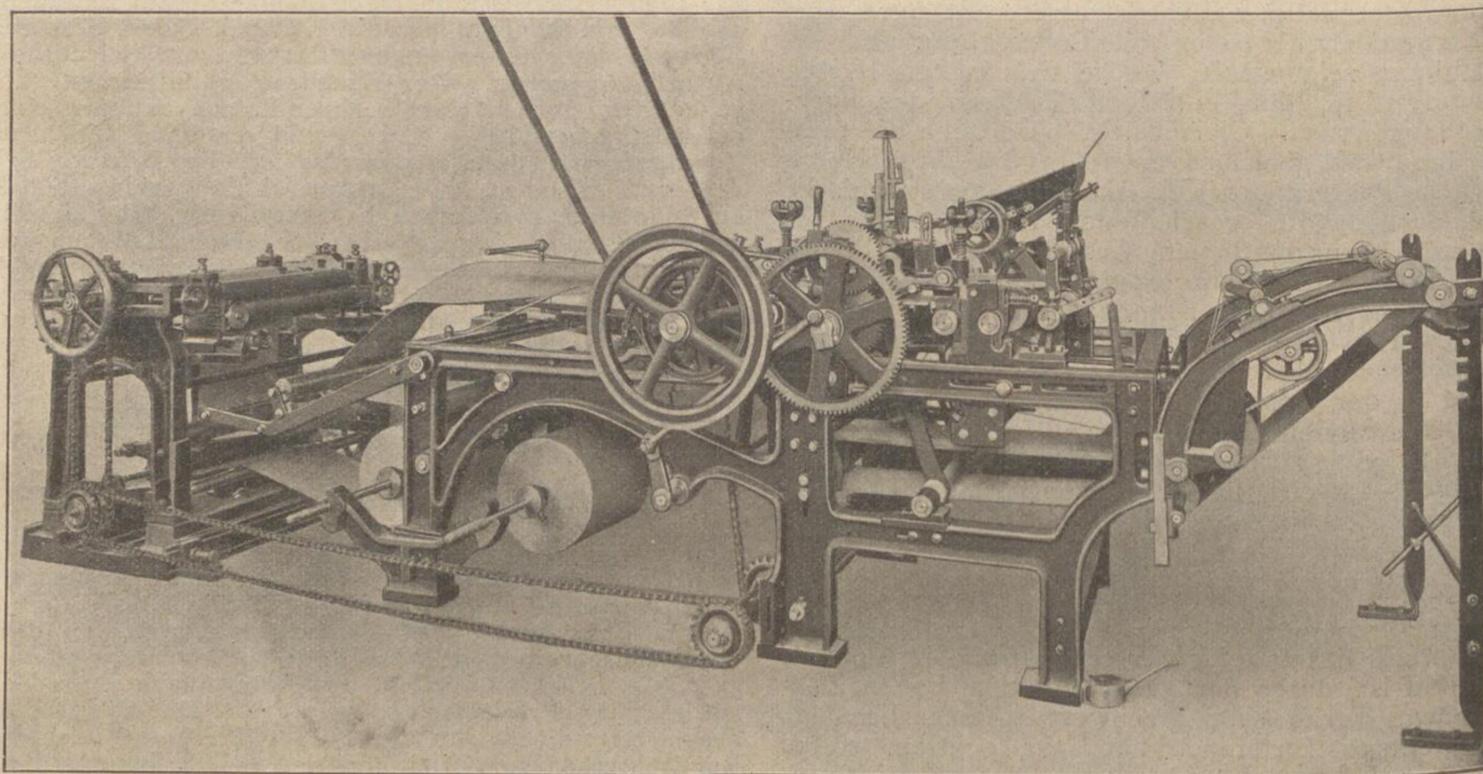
Kreuzbodenbeutel-Maschine mit Druckeinrichtung von C. Holweg & Co., Straßburg im Elsaß
